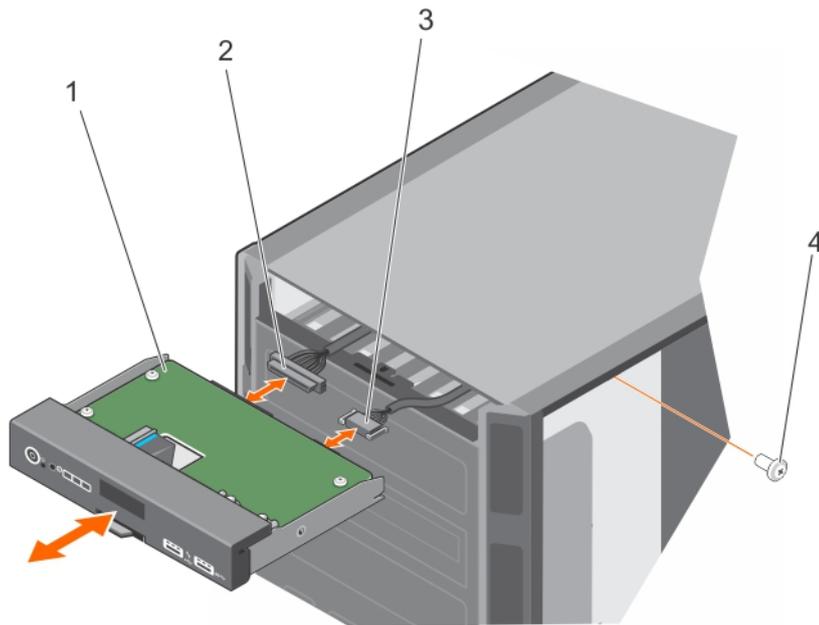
Entfernen und Installieren der Bedienfeldbaugruppe
